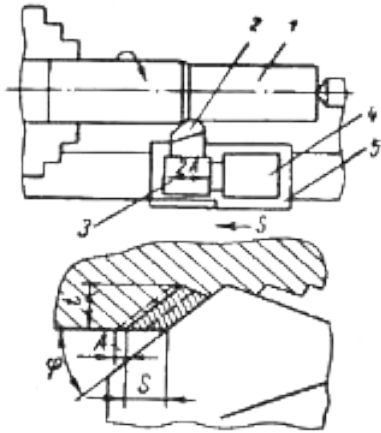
Схема вібраційного точення: 1 — заготовка; 2 — різець; 3 — різцетримач; 4 — гідравлічний вібраційний супорт; 5 — повздовжній супорт
